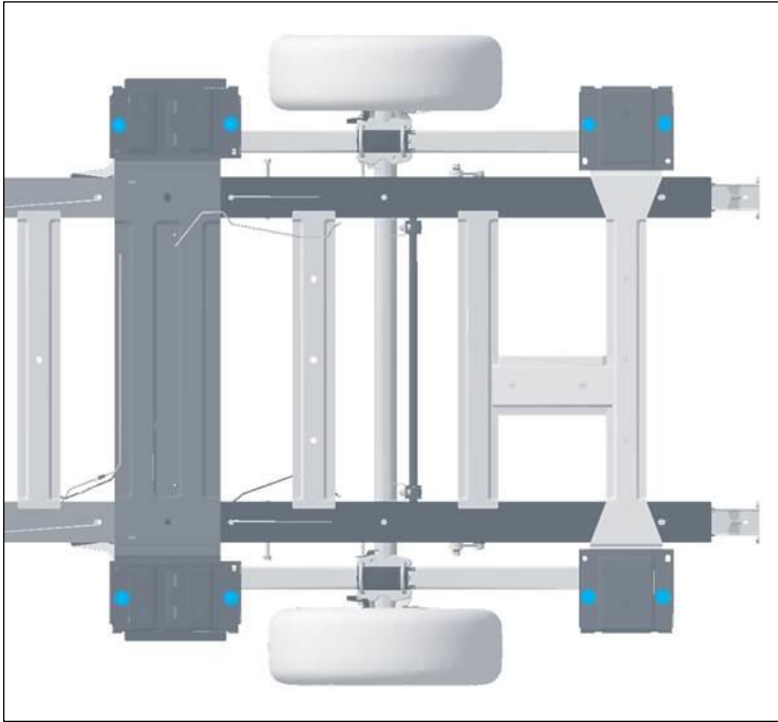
autotelaio Crafter a telaio piano - punti consentiti per collegamenti a vite (rappresentazione schematica della superficie del telaio)
